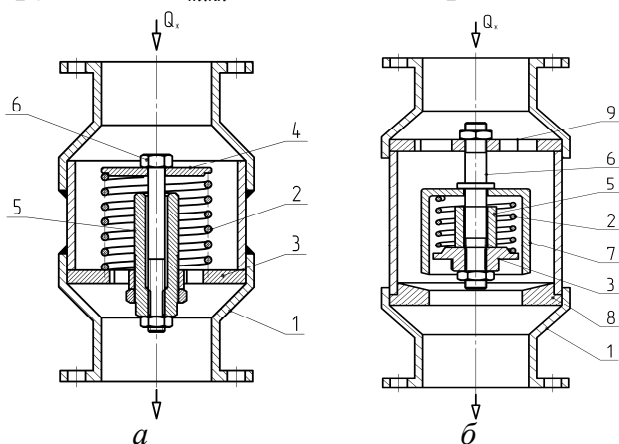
Расчетные схемы гасителей с пружинным (а) и со щелевым (б) дросселем: 1 – корпус; 2 – пружина; 3 – опора пружины; 4 – крышка; 5 – втулка-упор; 6 – шток; 7 – колпак; 8 – основание; 9- перфорированная пластина
